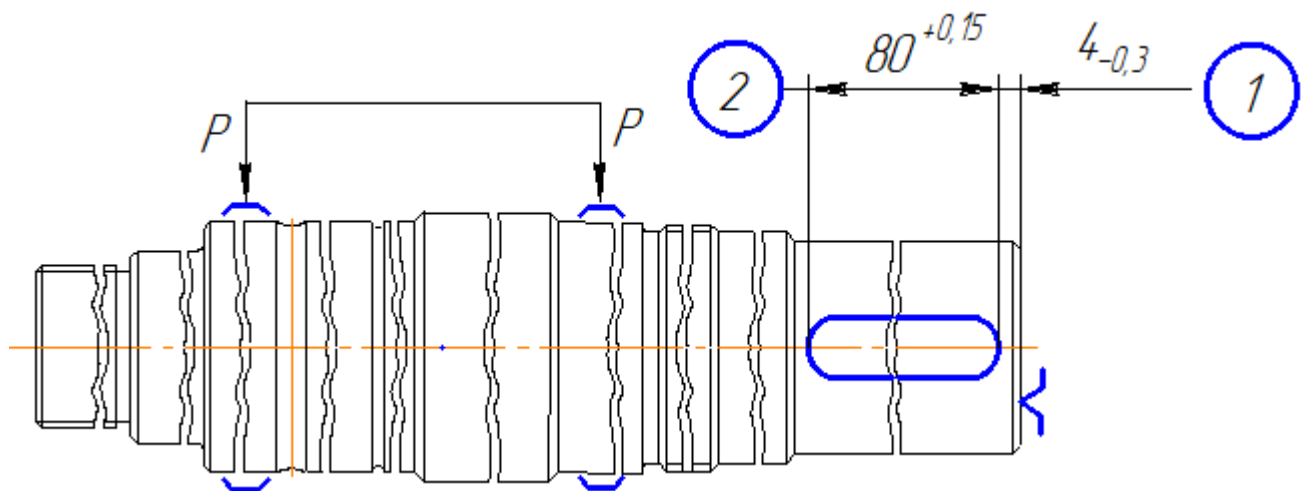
Базування вала на операції 035 (перехід 1)
